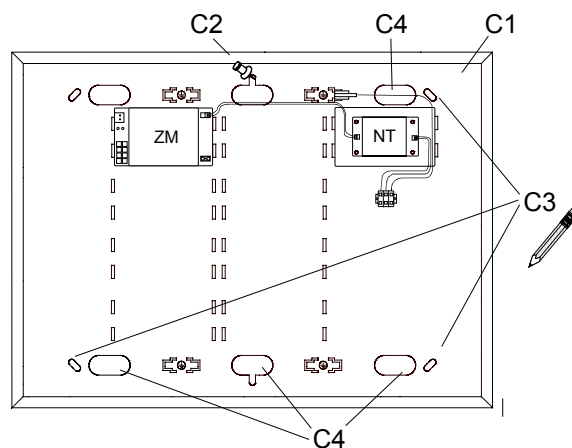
Anzeichnen der Bohrpositionen DIN A2
